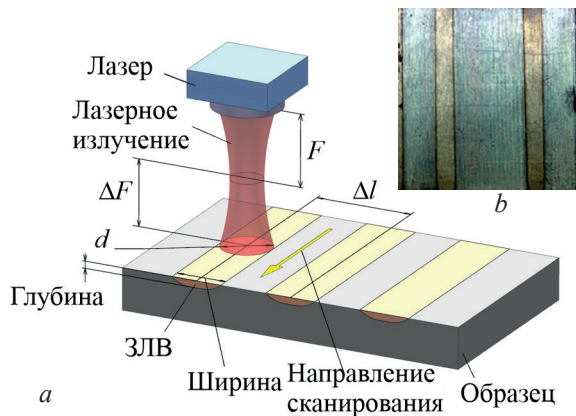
Схема обработки поверхности образцов сталей для металлографических исследований (а) и внешний вид подготовленной для испытаний на трение поверхности ЗЛВ образцов стали 12Х2Н4А (b).
